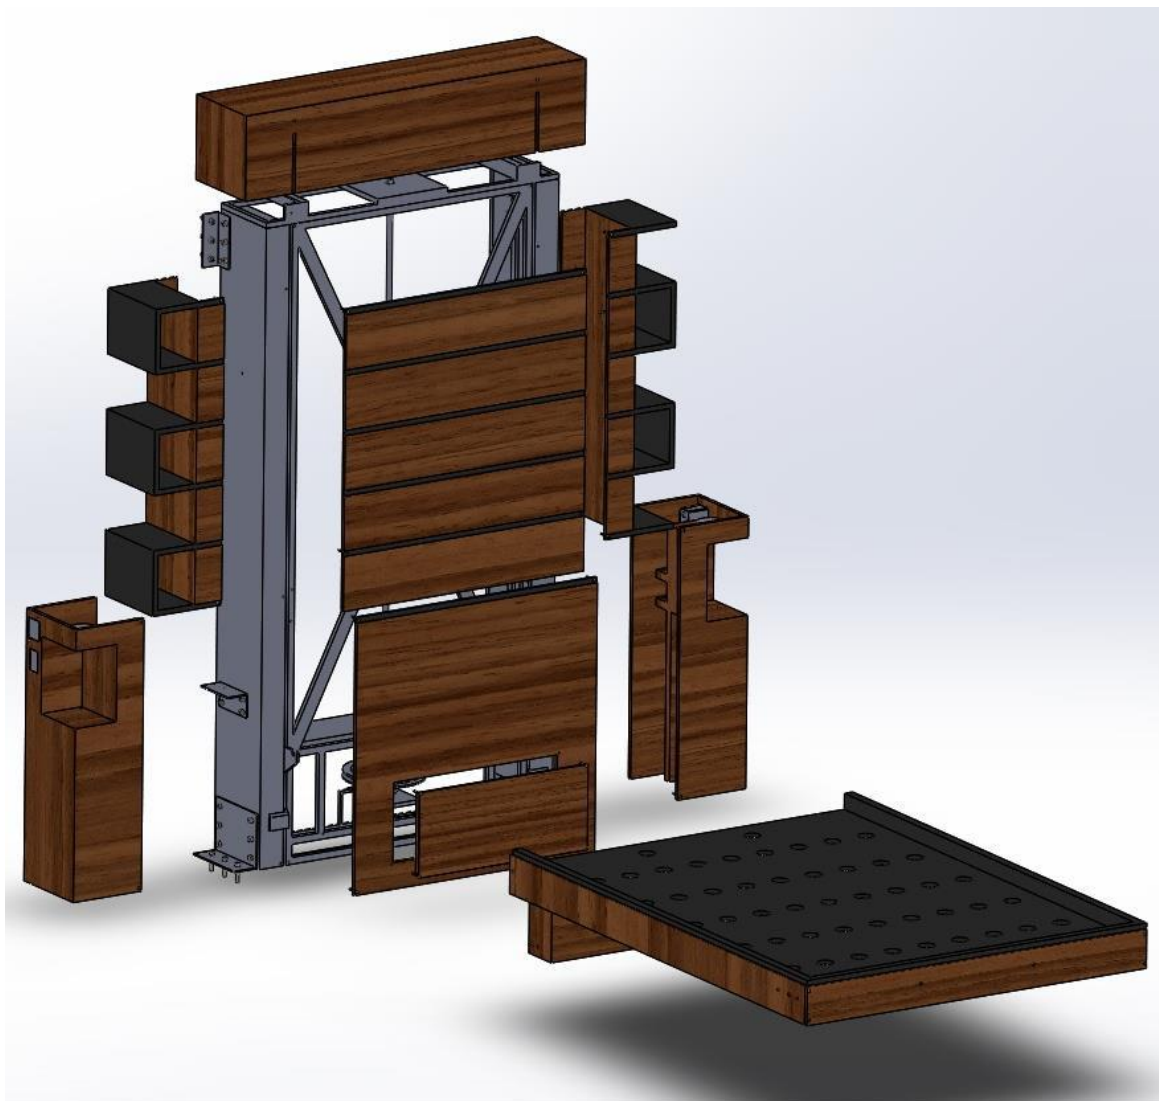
Vista Isométrica e Explodida dos conjuntos (Fonte: elaboração própria).
